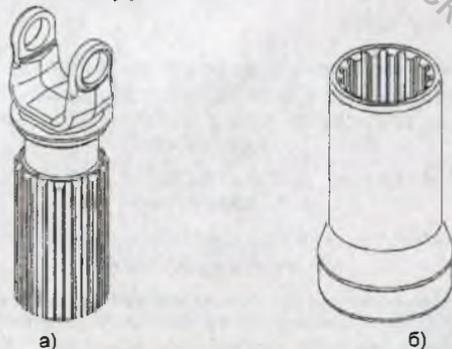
Внешний вид вилки скользящей (а) и втулки шлицевой (б)
